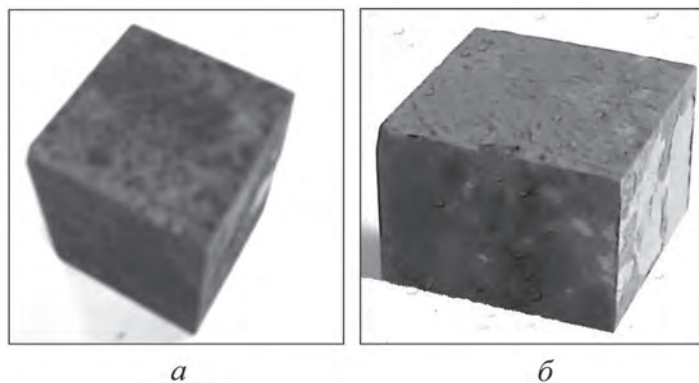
Модельный образец ножа ФТИ 5.001.1672 (40×40×23):
